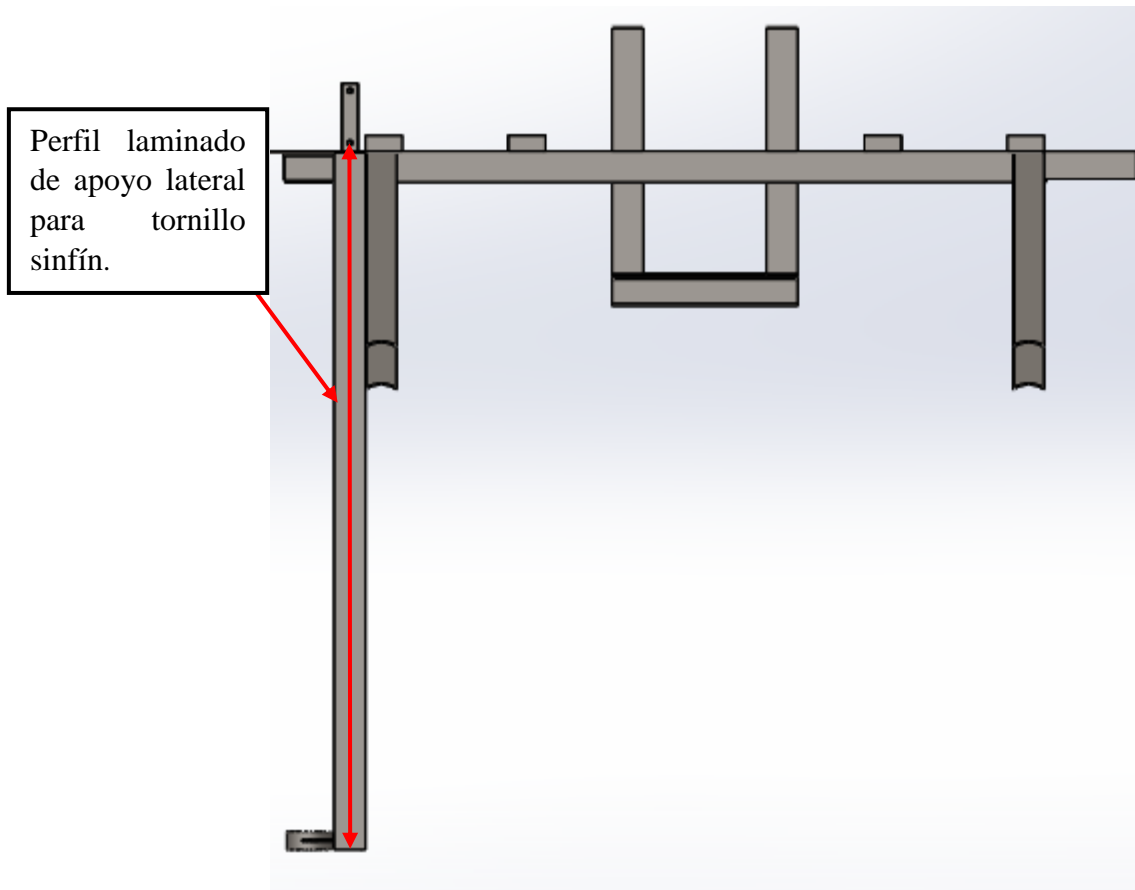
Ubicación de perfil vertical para desplazamiento de perfil en forma de U
